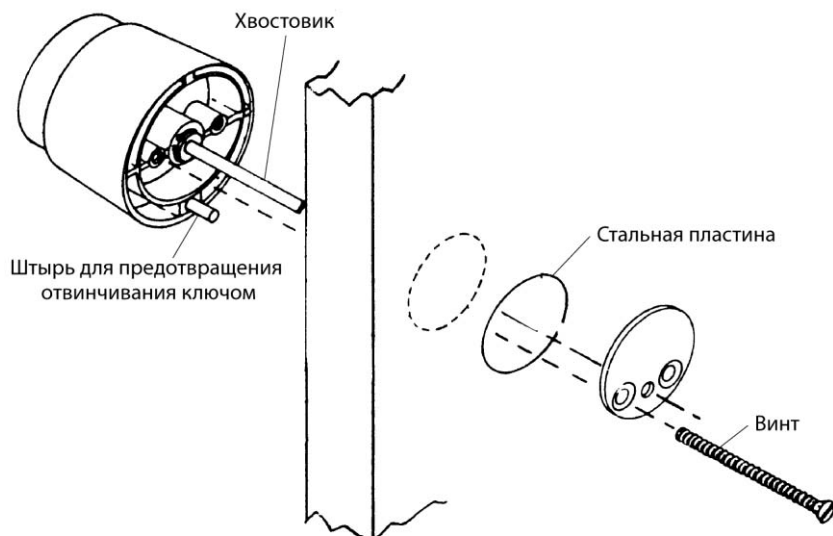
Детали комплекта Cor-Kit для накладного замка
